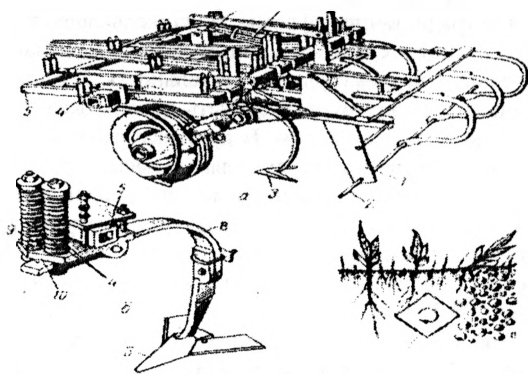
Культиватор КПЭ-3,8А со штанговым приспособлением: а — общий вид; б — рабочий орган; в — схема технологического процесса штанги; 1, 10 — кронштейны; 2 — штанга; 3 — стрельчатая лапа; 4 — пружины; 5 — рама; 6 — упор; 7 — гидроцилиндр; 8 — упругая стойка; 9 — болт.
